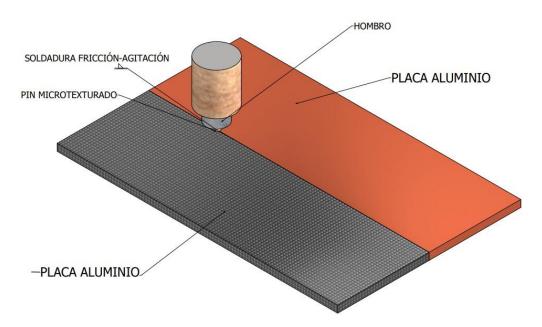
Prototipo de soldadura por fricción en placas de aluminio.
